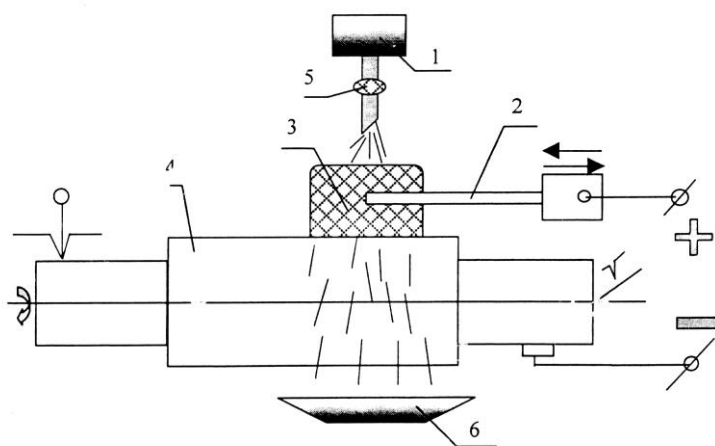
Схема установки для нанесения покрытий электролитическим натиранием на базе токарного станка.
